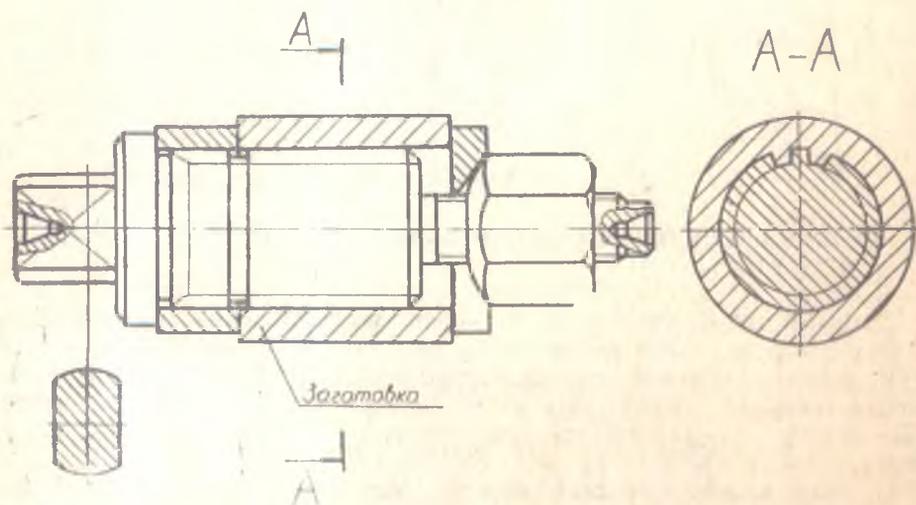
Оправка зубчатая (шлицевая) прямобочная
